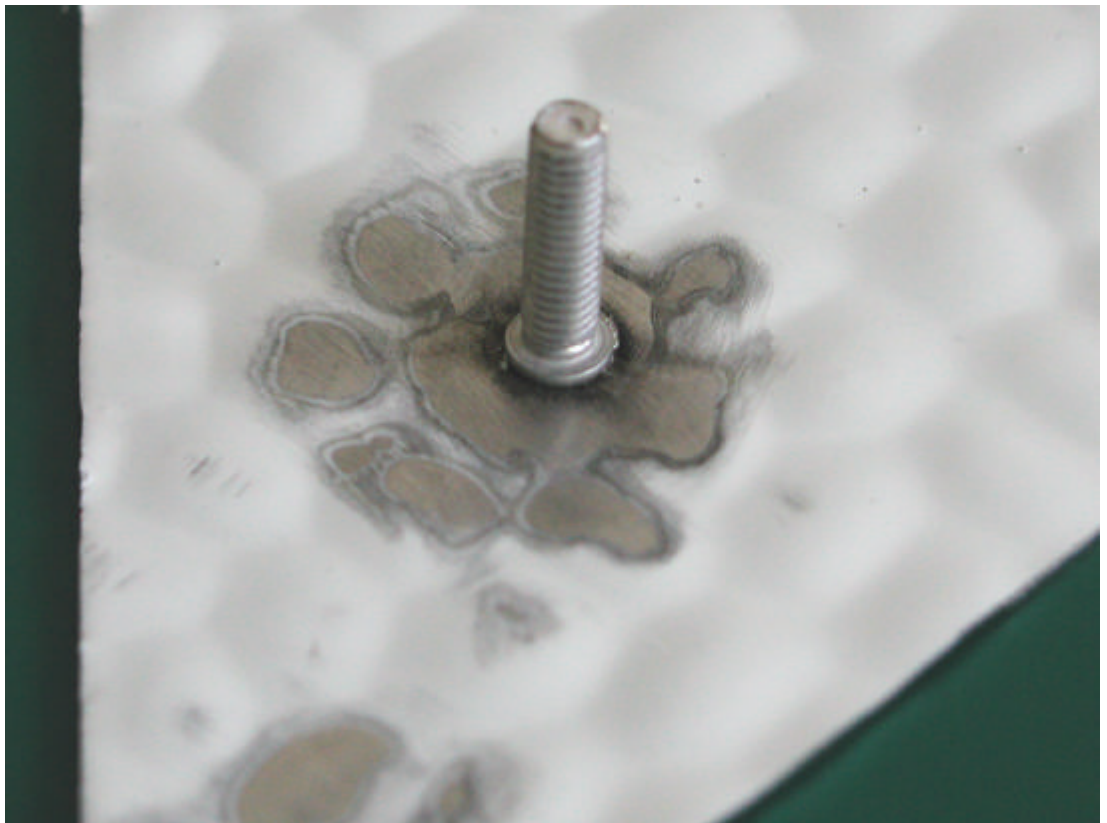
Angeschweißter Zugbolzen: nicht durchführbare Außenhautinstandsetzungsmethode
